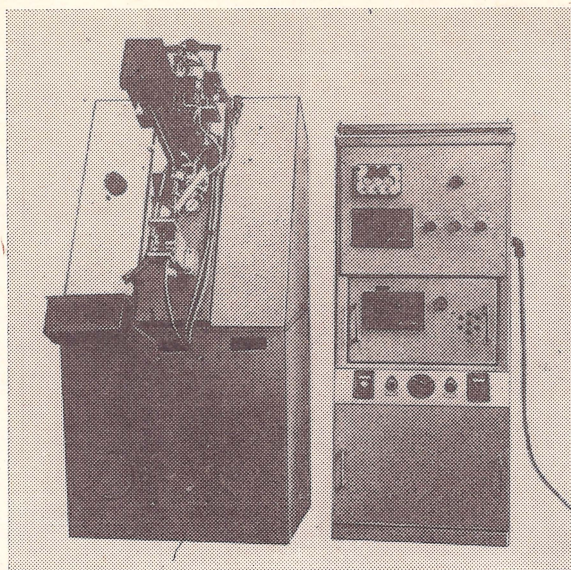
Доводочный станок-автомат ЦНИТА-8180 с полуавтоматической загрузкой деталей
